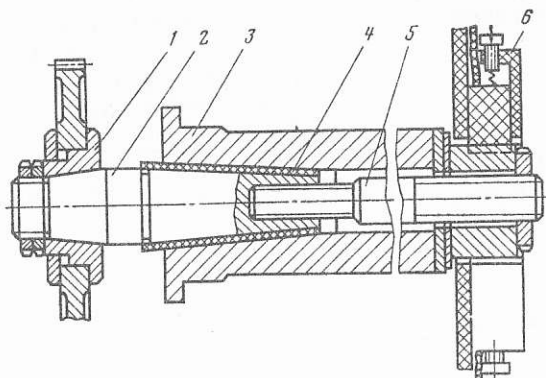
Устройство для подвода тока к кругу через полый шпиндель
